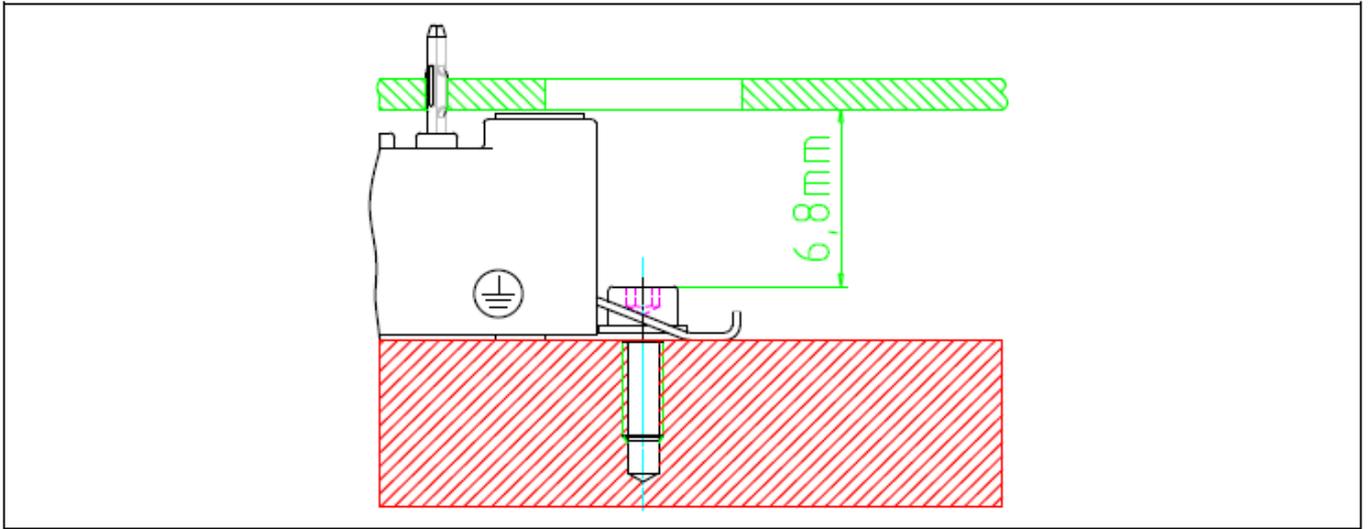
Easy1B 和 Easy2B 封装的夹具与 PCB 之间的空间距离
